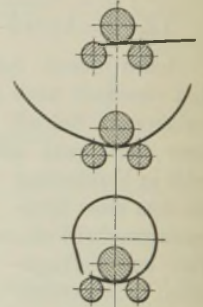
Das Biegen der Bleche auf der Blechbiegemaschine.
